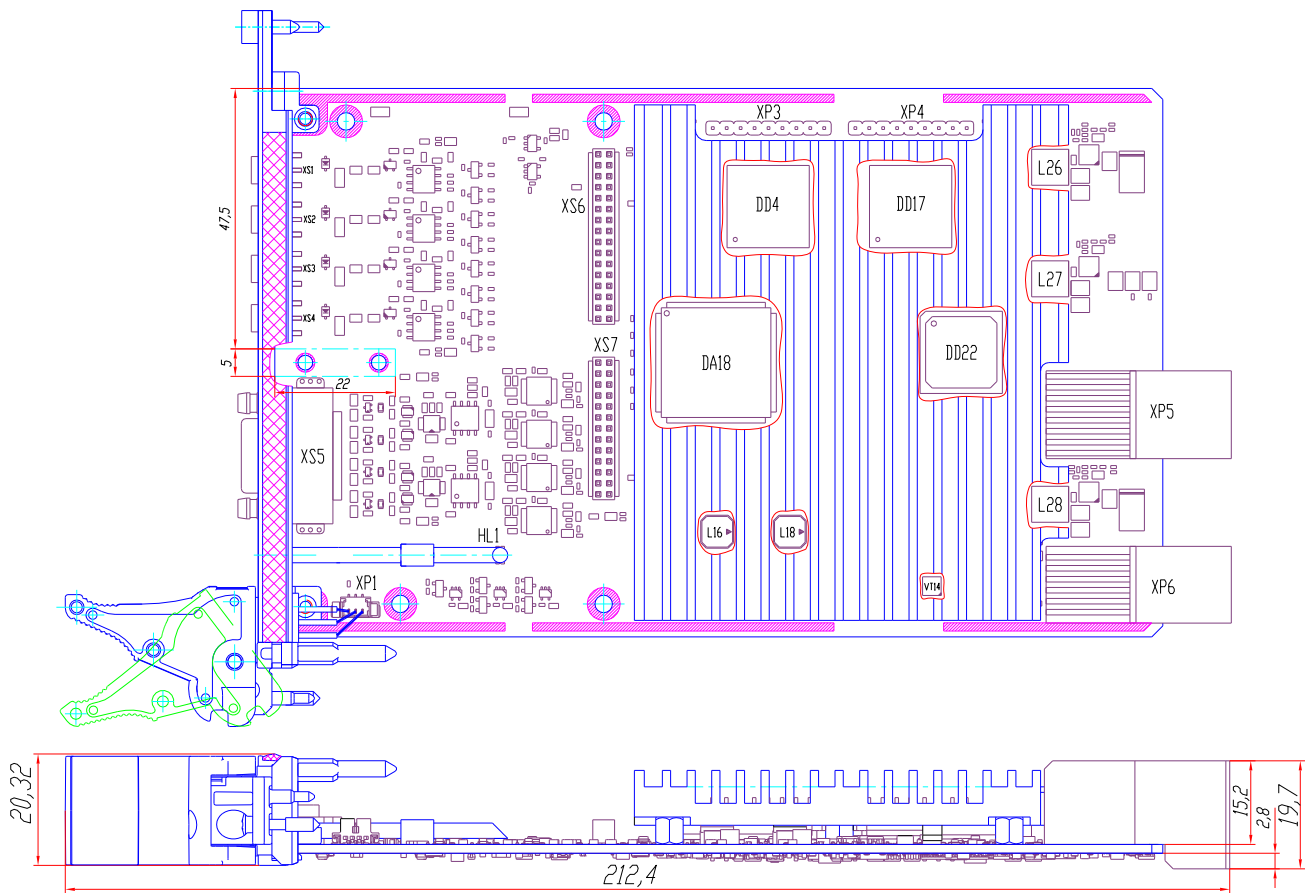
Габаритные размеры модуля VIM554 (вид сбоку приведен для исполнения VIM554-01-R1)
